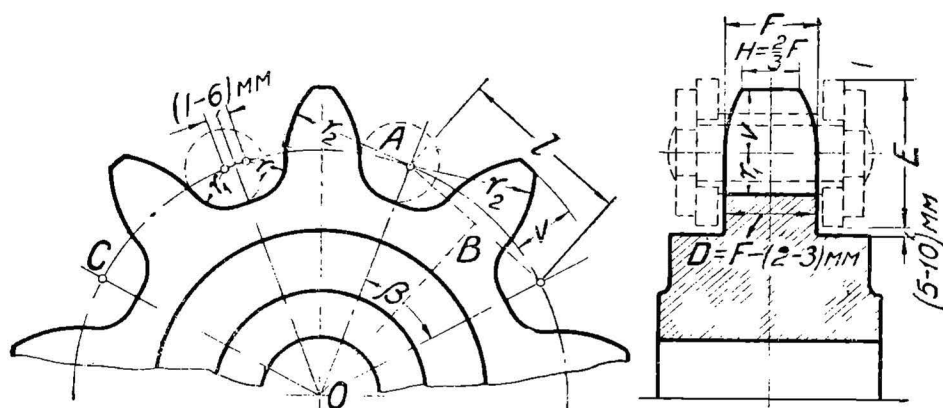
Схема ведущего блока для крючковой цепи Jeffrey.
